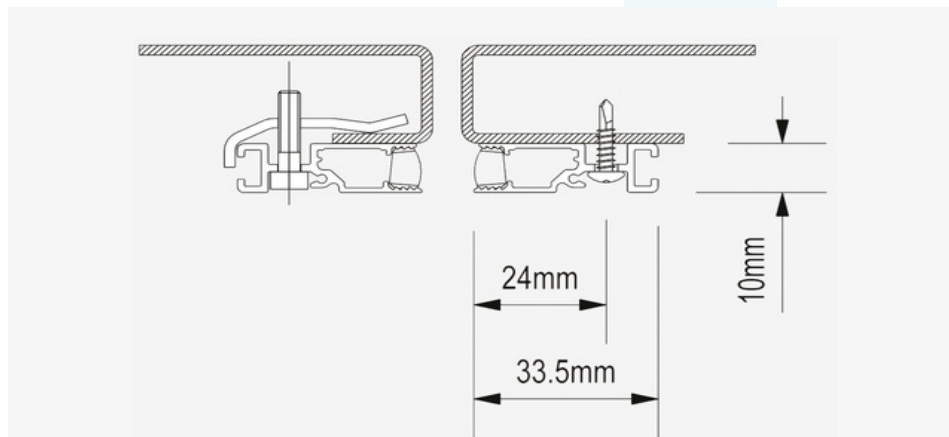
Morsetto di fissaggio E10 e vite autofilettante per apertura laterale e centrale
